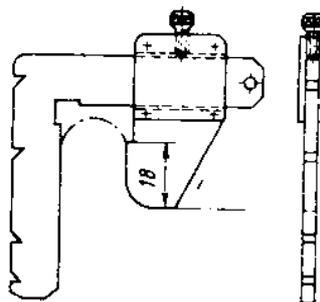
Шаблон для проверки вертикального подреза гребня колеса
